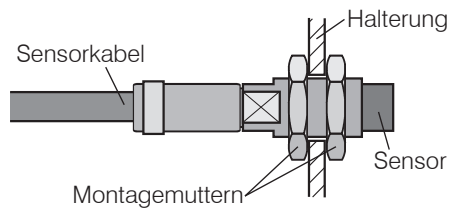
Ungeschirmter Sensor mit Gewinde in Standardmontage
